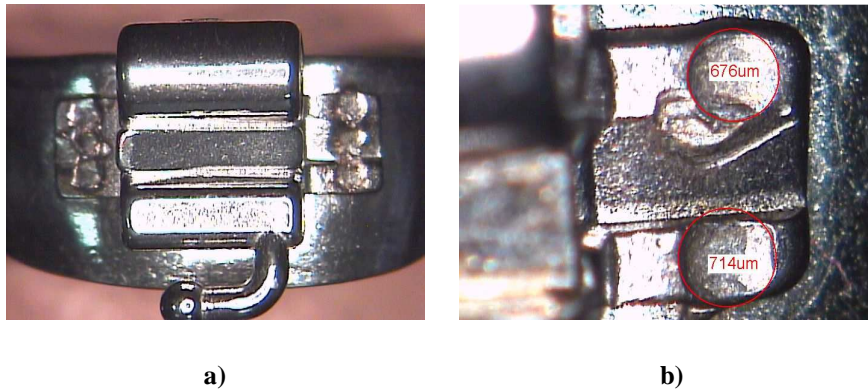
a) Photo und b) Vermessung der Schweißpunktdurchmesser mit dem Video-Mess-Inspektionssystem, Firma Jena Engineering
